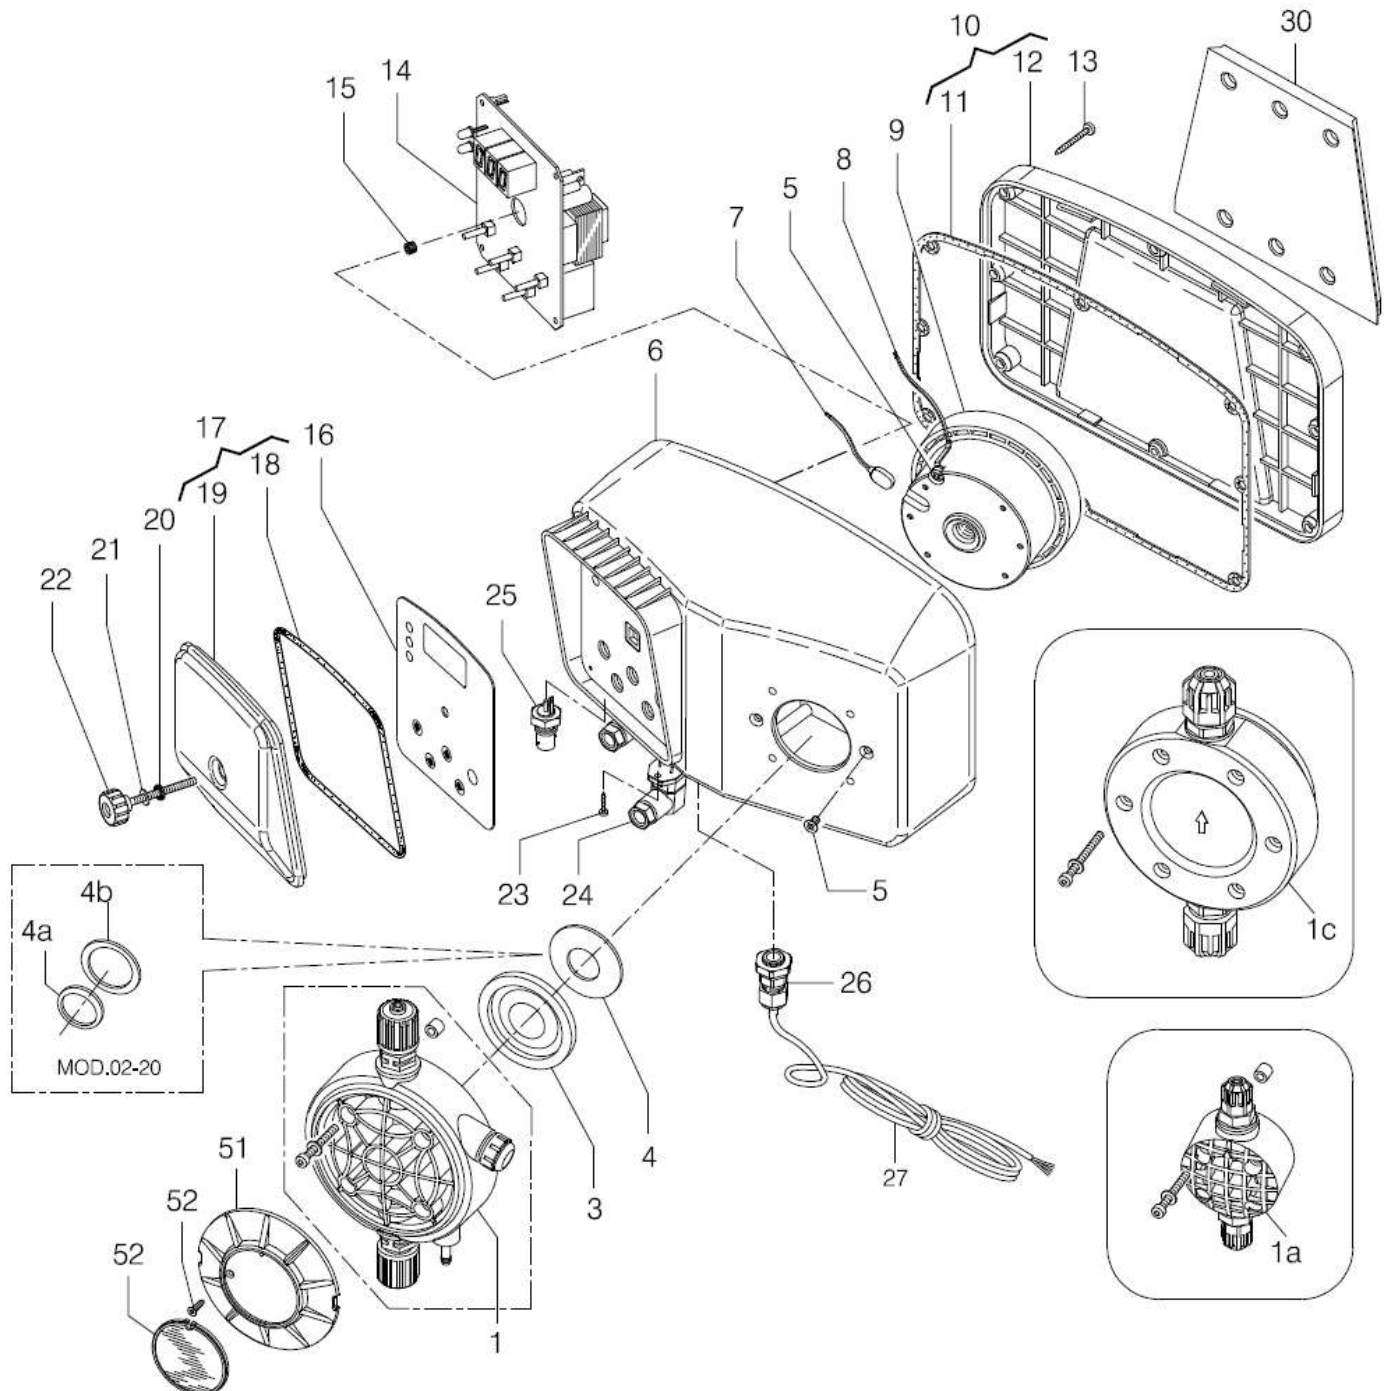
SERIE HC 2 - Esploso / Description / Explode / Dibujo / Чертеж
